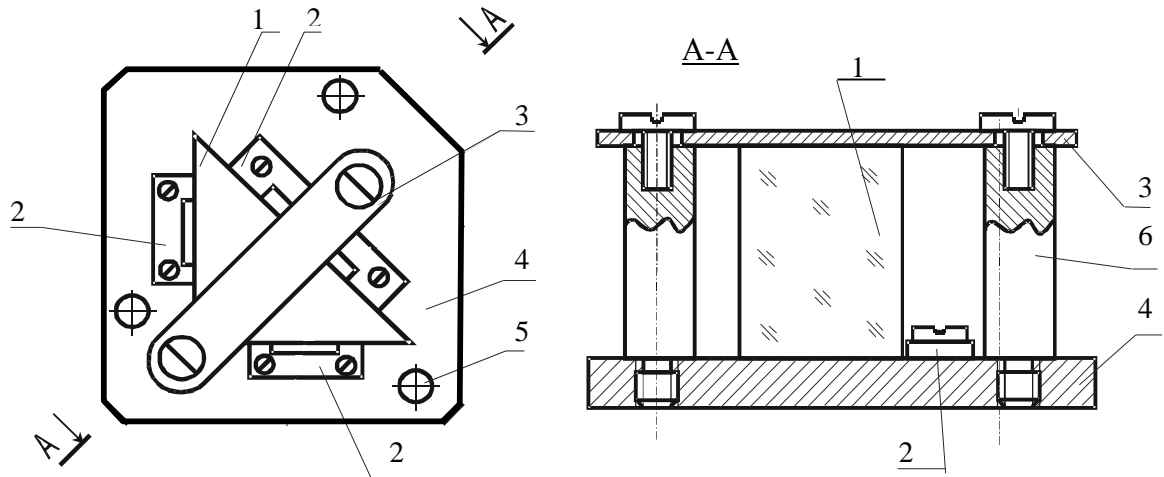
Кріплення притисною планкою: 1 – призма АР-90⁰; 2 – установочна планка; 3 – притискна планка; 4 – плато; 5 – отвір для кріплення плато; 6 – стійка
